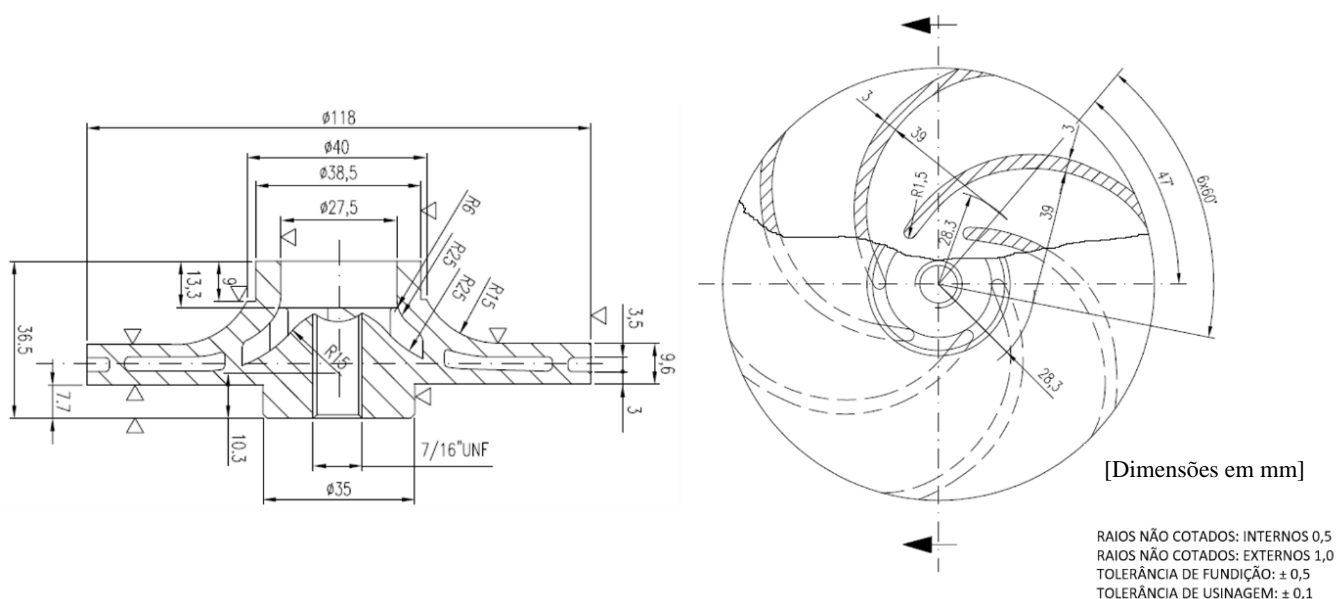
Desenho técnico bomba centrífuga SCX1 (Somar, 2005)
